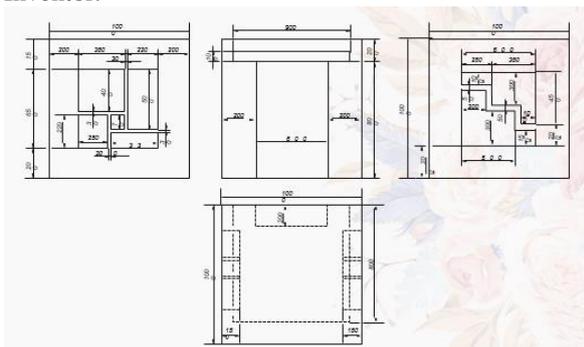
Сборочный чертеж в AutoCAD одного из модулей рабочего места
